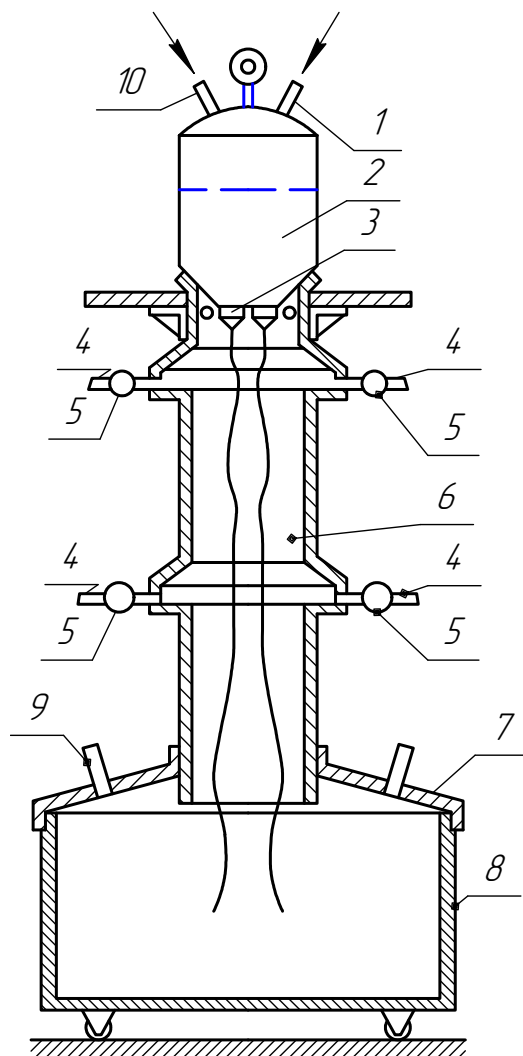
Схема установки для виготовлення неперервних металевих волокон способом екструзії: 1, 9, 10 – штуцери; 2 – ємкість; 3 – отвір; 4 – трубка; 5 – вентиль регулювальний; 6 – камера; 7 – зонт витяжний; 8 – бункер
